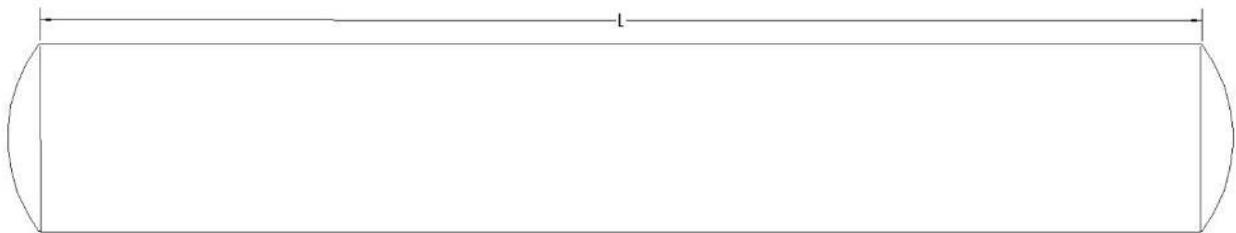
Croquis de la geometría principal del equipo. Fuente: Elaboración propia.
